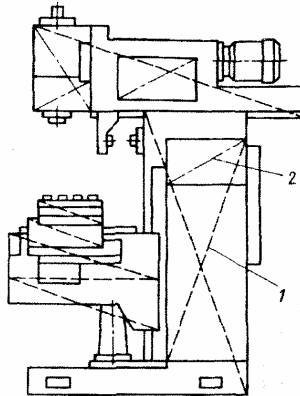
Графическая схема пропорции элементов консольно-фрезерного станка
